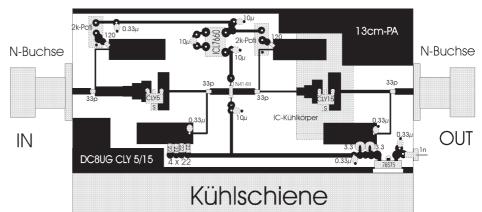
Layout mit Bestückungsplan, Ansicht von der Printseite
